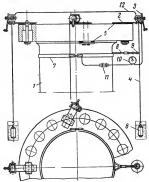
Приспособление для центровки вала турбины по струнам,
